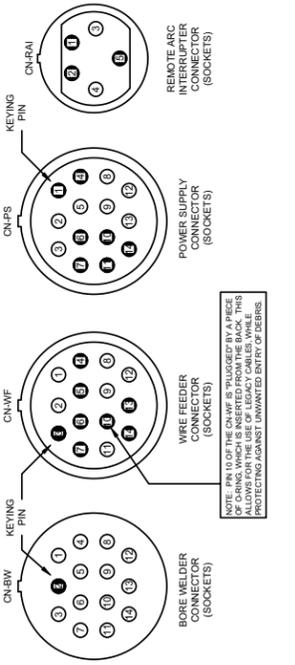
Пластиковые разъемы контроллера 170, схема 1 (кат. № 98041)
